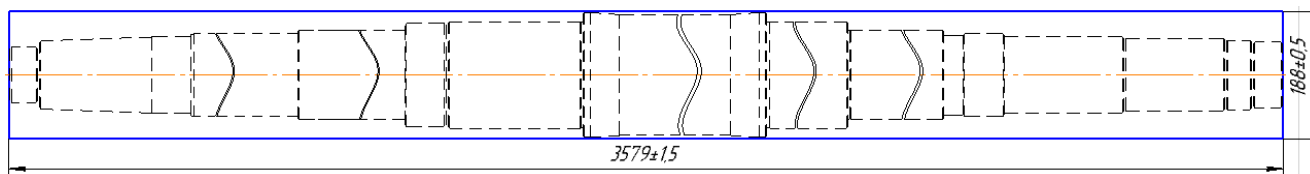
Вигляд заготовки, що отримується прокатом
